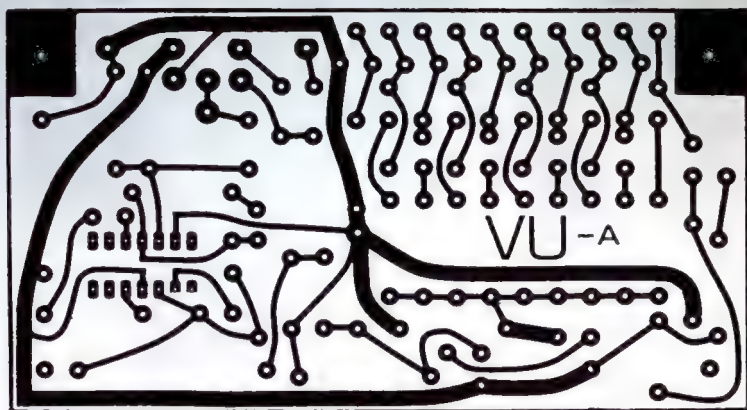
Die Abmessungen des Prints wurden für das Modulsystem passend gewählt.
